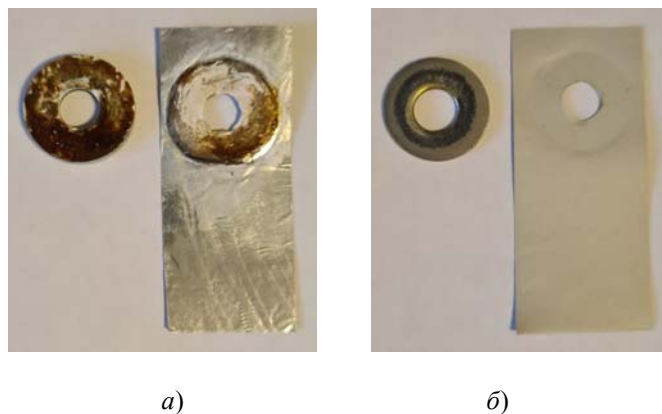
Разобранный конструктивно-подобный образец после испытаний на коррозию без покрытия (а) и с покрытием (б)
